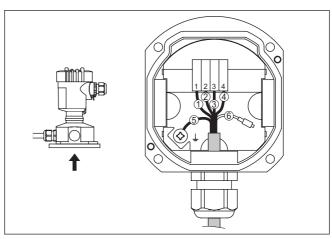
Anschluss der Prozessbaugruppe im Gehäusesockel
